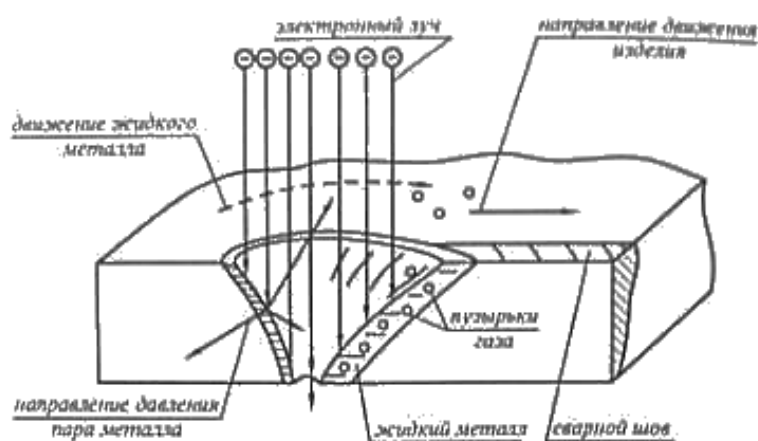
Схема формирования сварного шва при электронно-лучевой сварке
